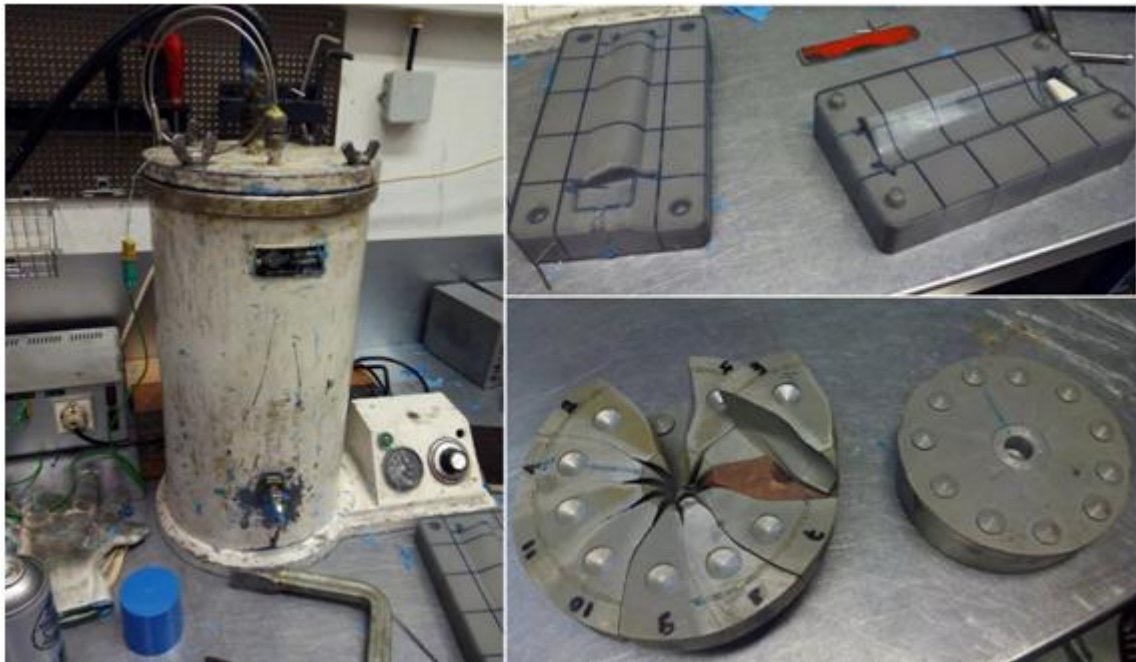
Equipamento de injeção de cera/moldes do INEGI
